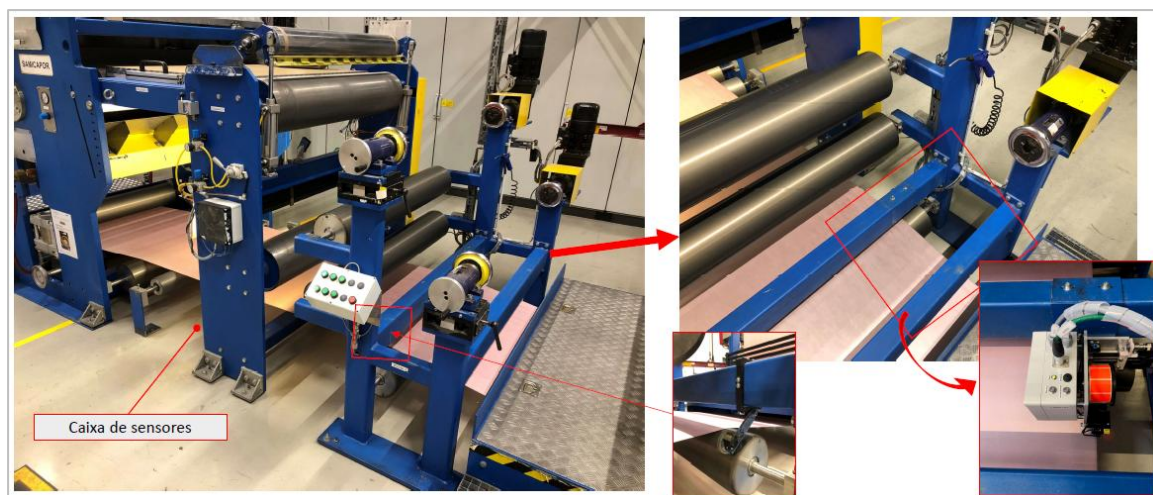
Fotos do layout de instalação de todos os componentes na Laminadora
